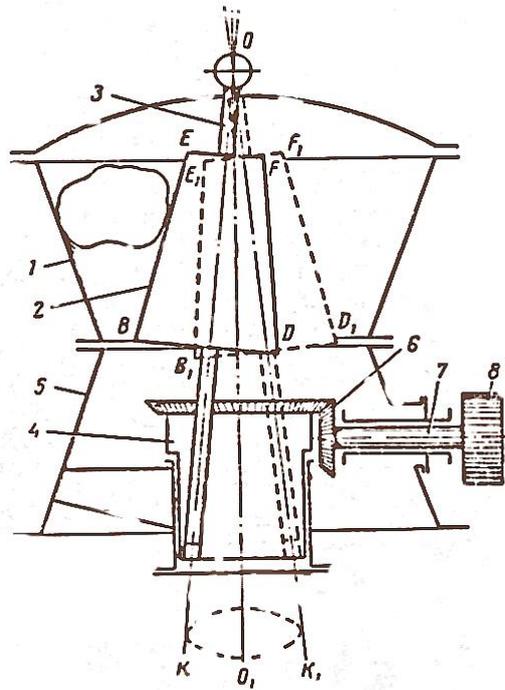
Схема конусной дробилки для крупного дробления с подвешенным валом (ККД): 1 – верхняя часть станины (неподвижная коническая чаша); 2 – дробящий конус; 3 – вал; 4 – эксцентриковый стакан; 5 – нижняя часть станины; 6 – коническая передача; 7 – приводной вал; 8 – шкив
